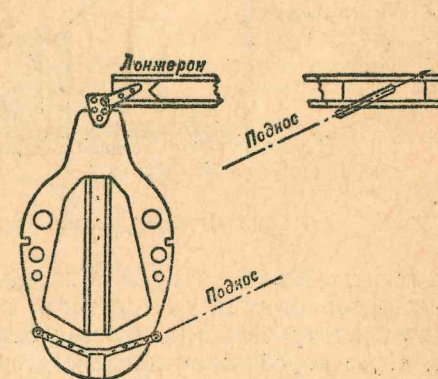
Центральный шпангоут круглого фюзеляжа и схема крепления к нему крыла у подкосного планера Г-9
